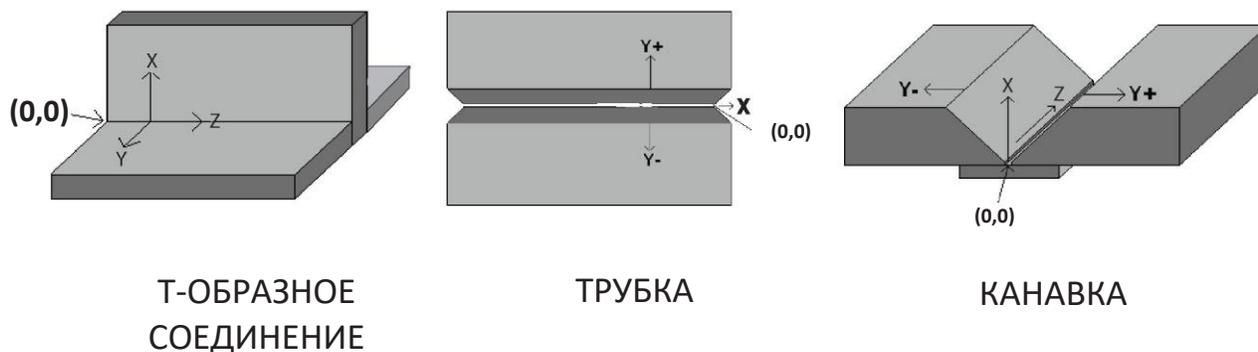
Координатная карта для размещения сварного шва (положение)
